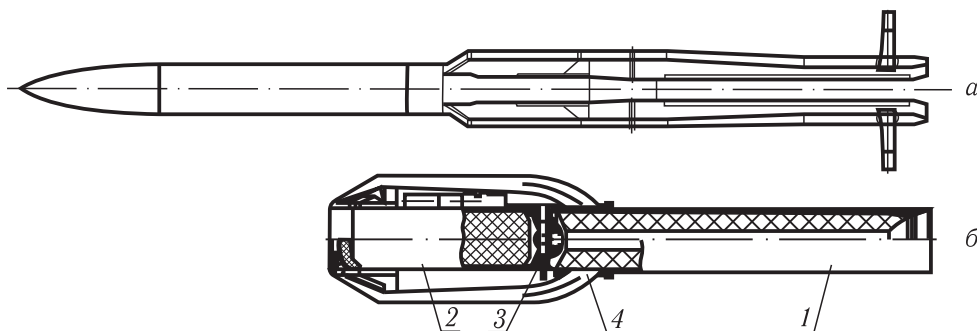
Комбинированный ракетно-прямоточный двигатель для ракет класса «воздух–воздух»: 1 — стартовый двигатель; 2 — маршевый газогенератор, 3 — переходный отсек; 4 — воздухозаборное устройство. Внешний вид — а, сечение двигателя — б
